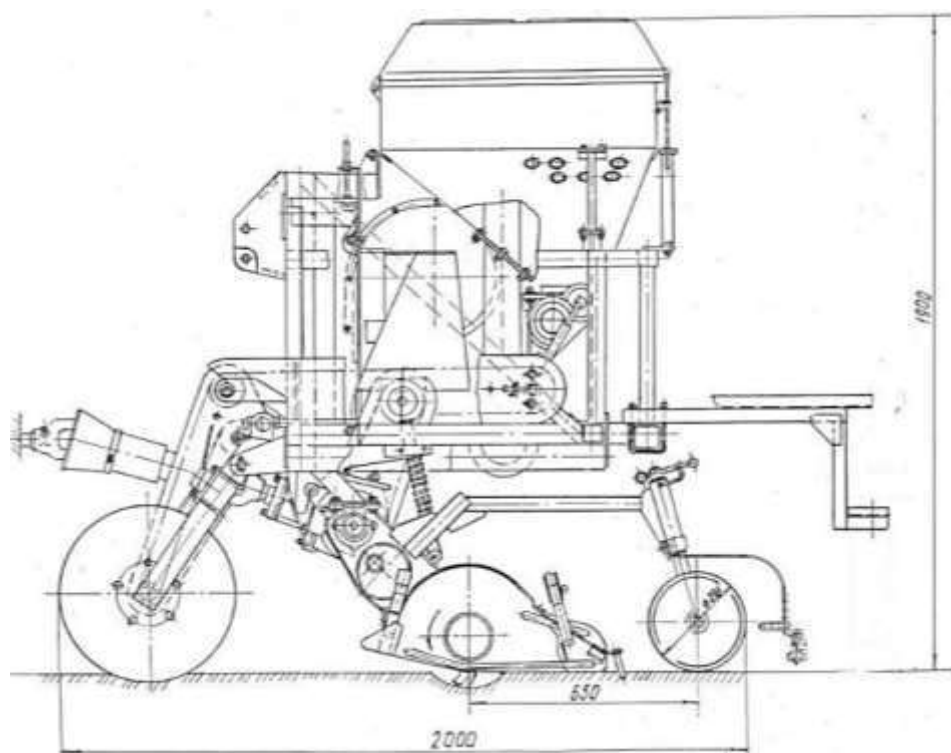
Конструктивная схема макетного образца агрегата МПТД-12 модульного построения
